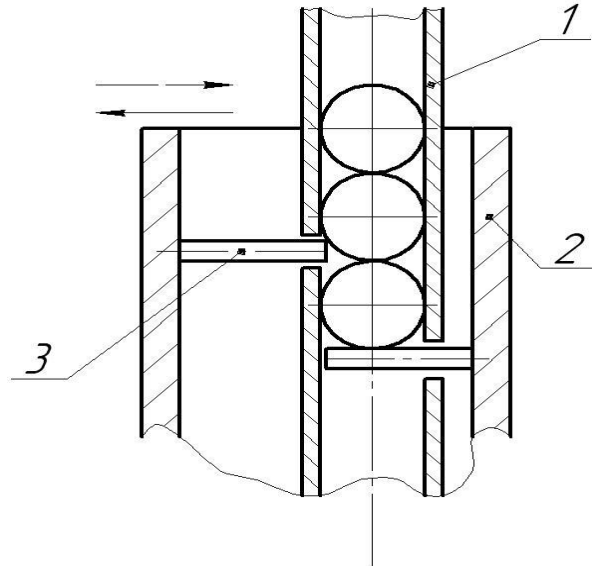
Штифтовий відсікач: 1 – магазин-накопичувач зорієнтованих заготовок; 2 – корпус відсікача; 3 – штифти для відокремлення заготовки
